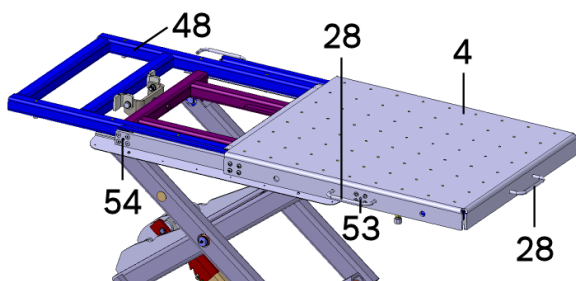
Justera utrymmet mellan den utdragbara plattformen och den övre ramen
